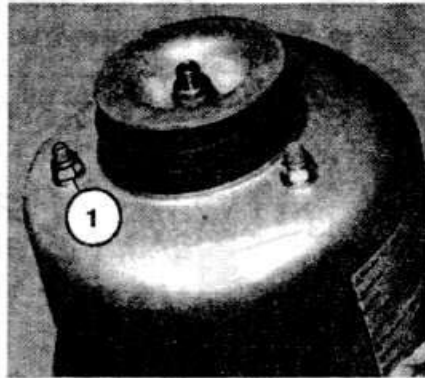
Гайка 1 крепления верхней опоры стойки подвески к кузову
